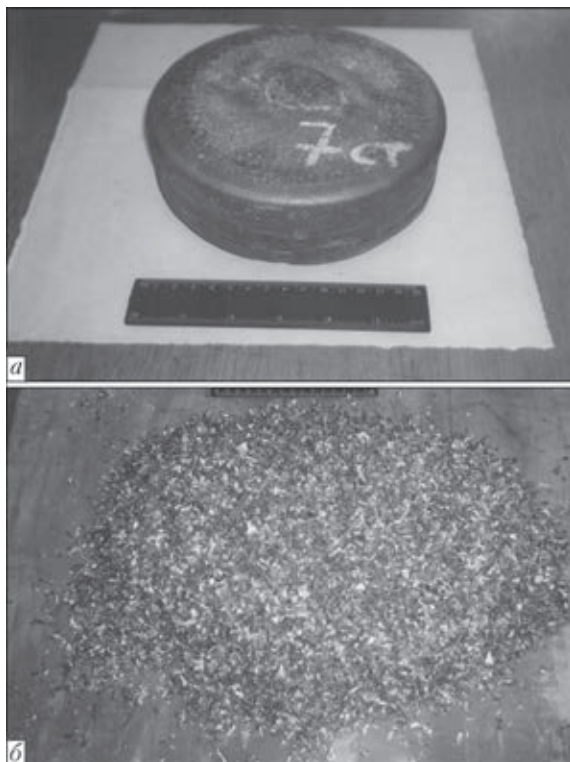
Внешний вид плавленной заготовки (а) и дискретная наплавочная присадка — стружка стали 15X11МФ (б) (опыт № 4, табл. 3)
